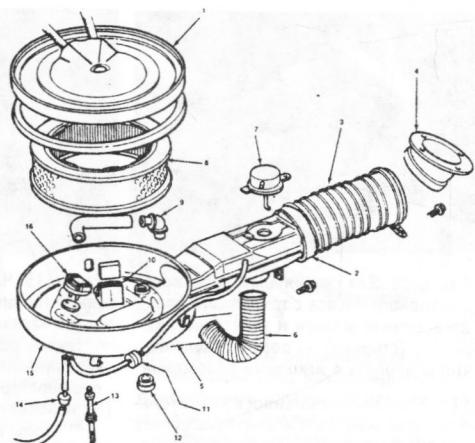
а Сборка воздухоочистителя — покомпонентное изображение (двигатель с четырьмя цилиндрами)
